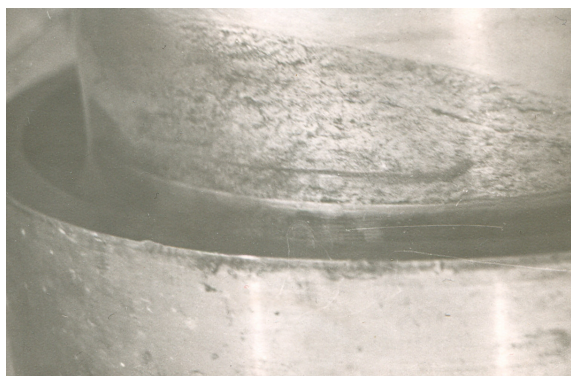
Общий вид зоны фреттинг-процесса на валу компрессора
